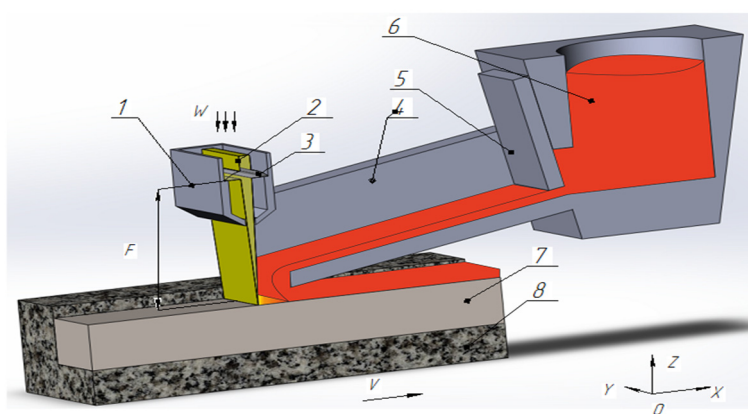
Схема реалізації лазерно-ливарного способу створення біметалів:
